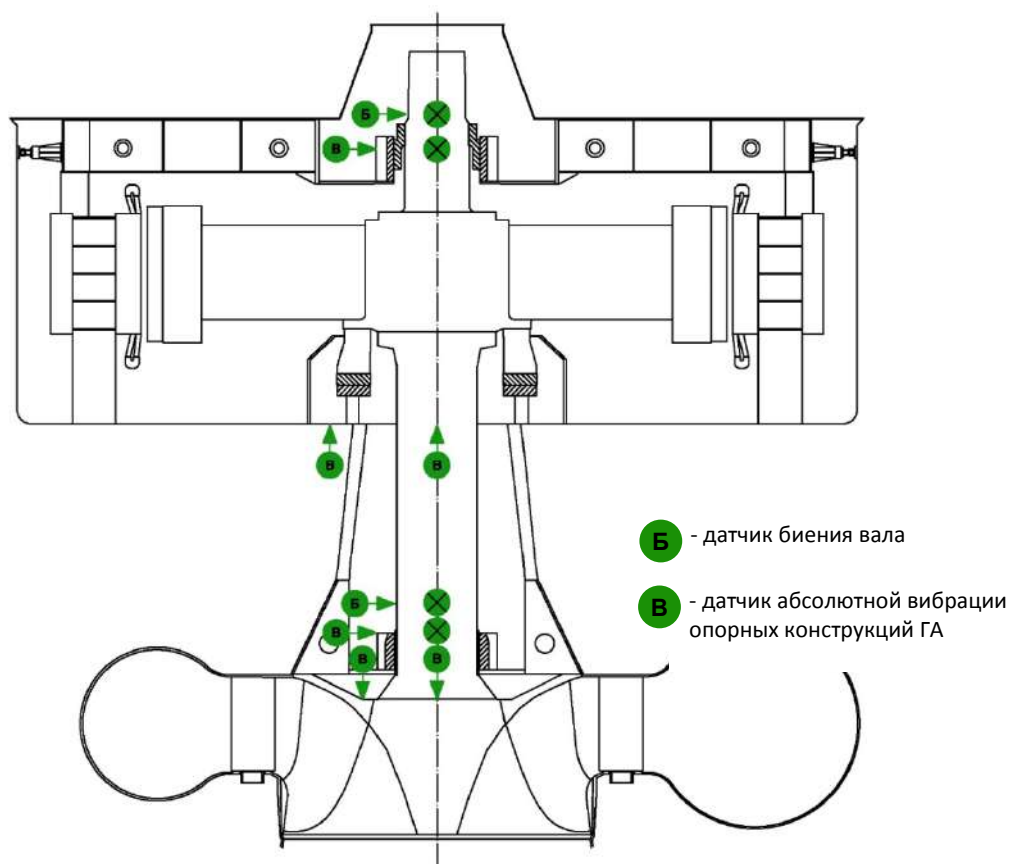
Схема расстановки датчиков биения вала и вибрации опорных конструкций ГА
